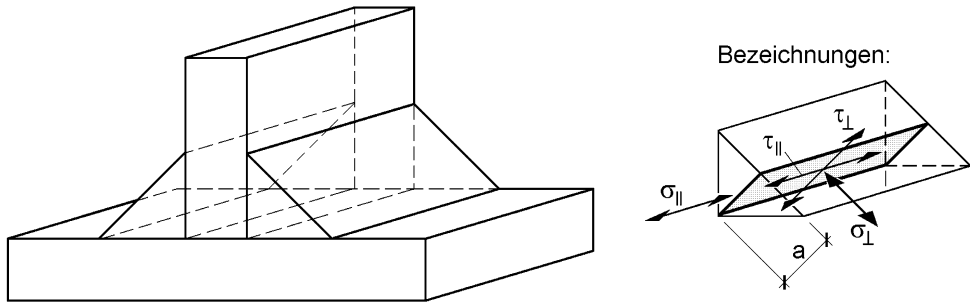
Schweißnahtspannungen im schrägen Schnitt in einer Kehlnaht [97]
